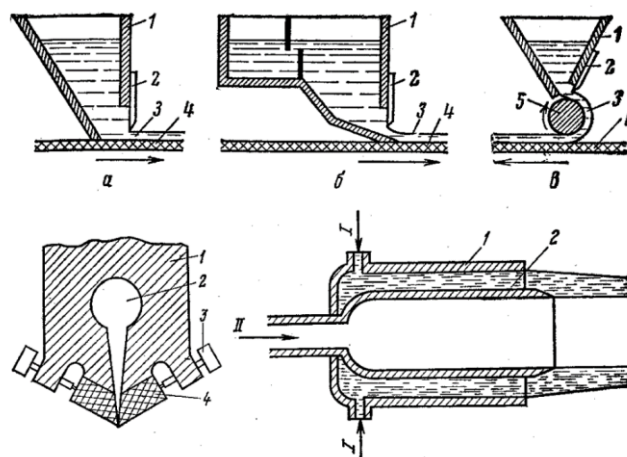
Схемы фильер для формования мембран: а-намазывающего типа; б - льющая; в - с валиком; г - щелевая; д - кольцевая; а-в: 1 - корпус фильеры; 2 - подвижная планка (нож); 3 - формовочный раствор; 4 - движущаяся подложка; 5 - валик; г: 1 - корпус; 2 - полость для раствора; 3 - регулировочный винт; 4 - подвижная пластина; д: 1 - наружный слой; 2 - внутренний слой; 1 - формовочный раствор; 11 - осадитель
